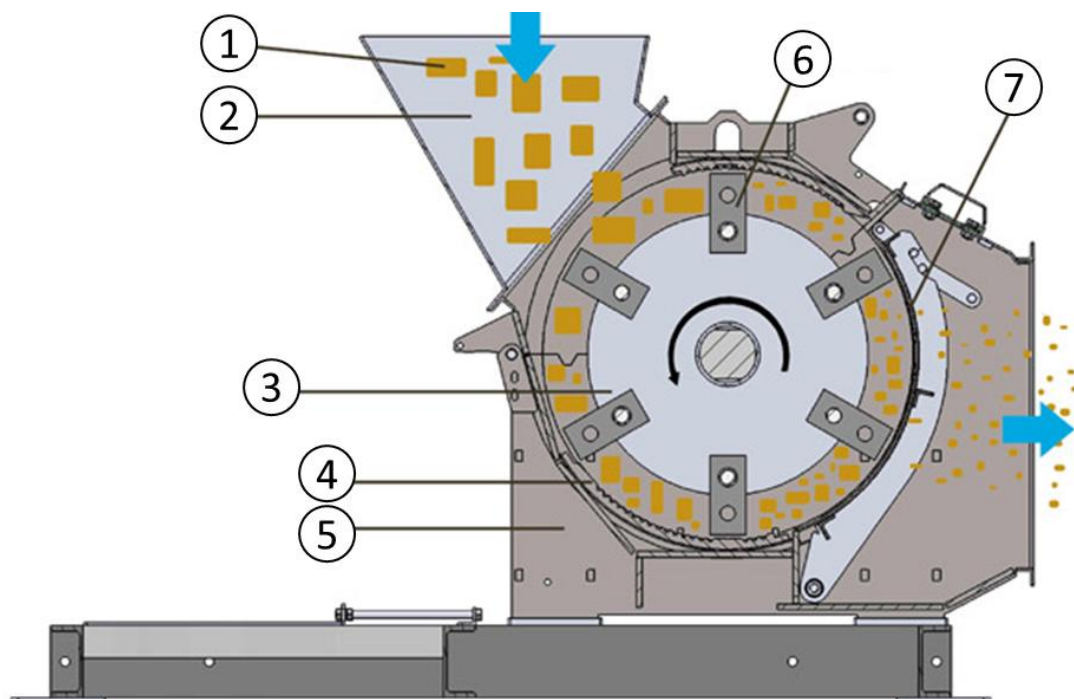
Схема молоткової дробарки: 1 – зерно; 2 – приймальна горловина; 3 – ротор; 4 – дека; 5 – корпус; 6 – шарнірно підвішений молоток; 7 – решето (класифікатор)
